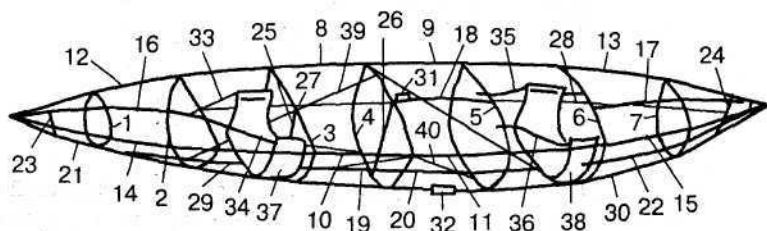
Каркас КНБ-81: 1-7 — шпангоуты; 8-11 — привальные брусья; 12-15 — штевневые окончания привальных брусьев; 16-18 — мидельвейсы; 19-20 — кильсон; 21-22 — штевни; 23-24 — штевневые пиллерсы; 25-26 — пиллерсы шпангоутов; 27-30 — опорные тросики; 31-32 — крепления опорных тросиков; 33-34 — тросики-упоры; 35-36 — трубчатые упоры; 37-38 — банки; 39-40 — тросики усиления
